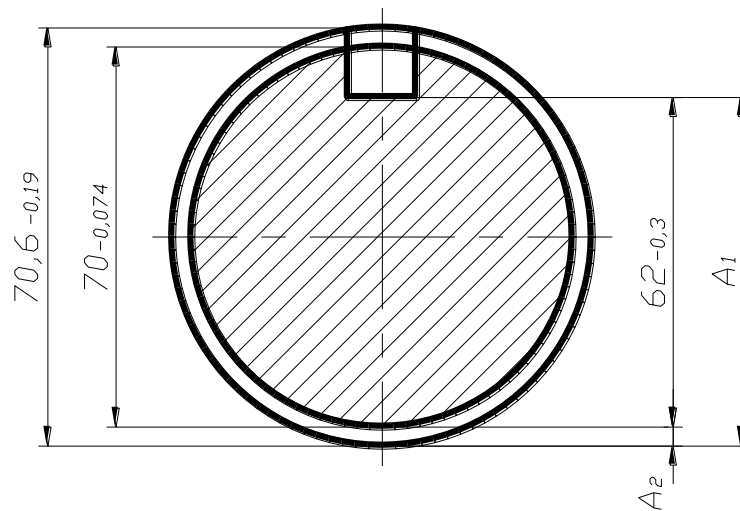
Схема шпоночного паза з розмірними параметрами
